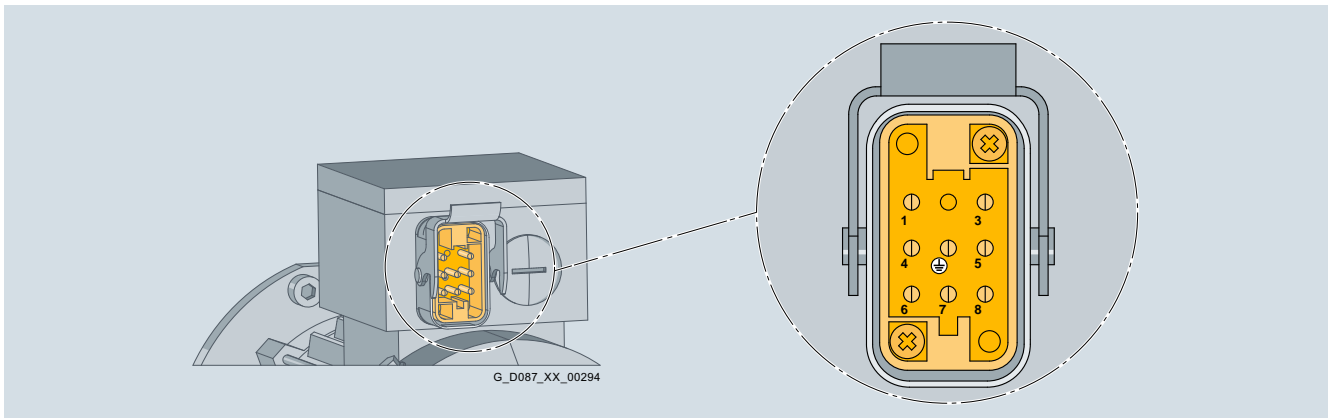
/23 Motorstecker HAN Q8 mit Pinbelegung bei Motorbaugröße 63 und 71
